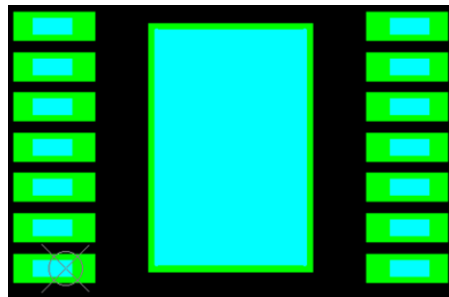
PWP0014L on SO-14 PCB Pad, Light blue: PWP0014L leads, Green: Other SO-14 PCB Pad
